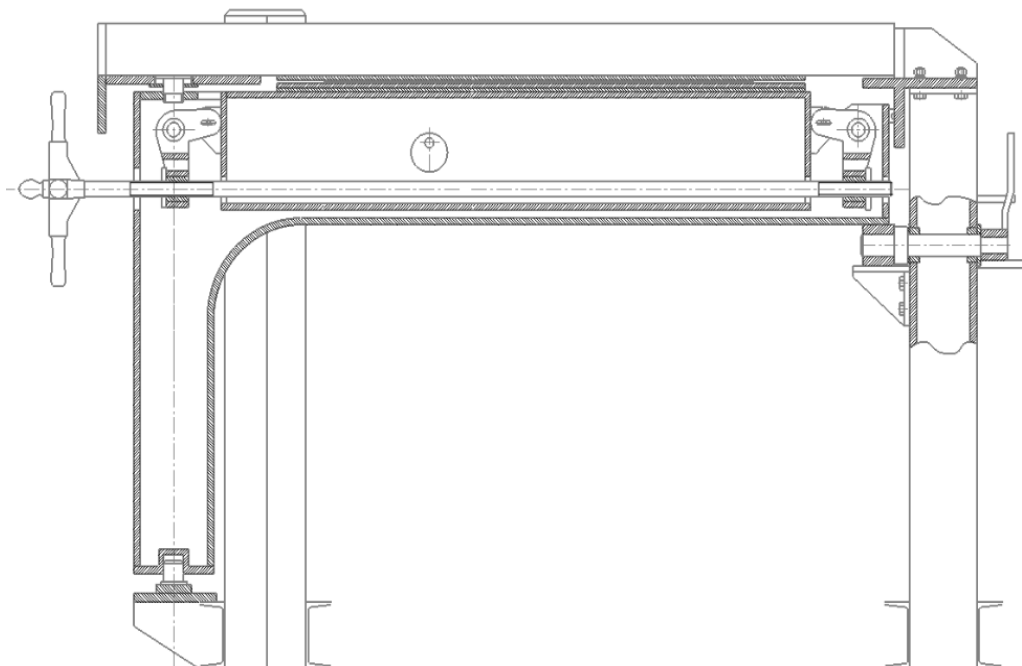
Установка для зварювання поздовжнього шва [24]
